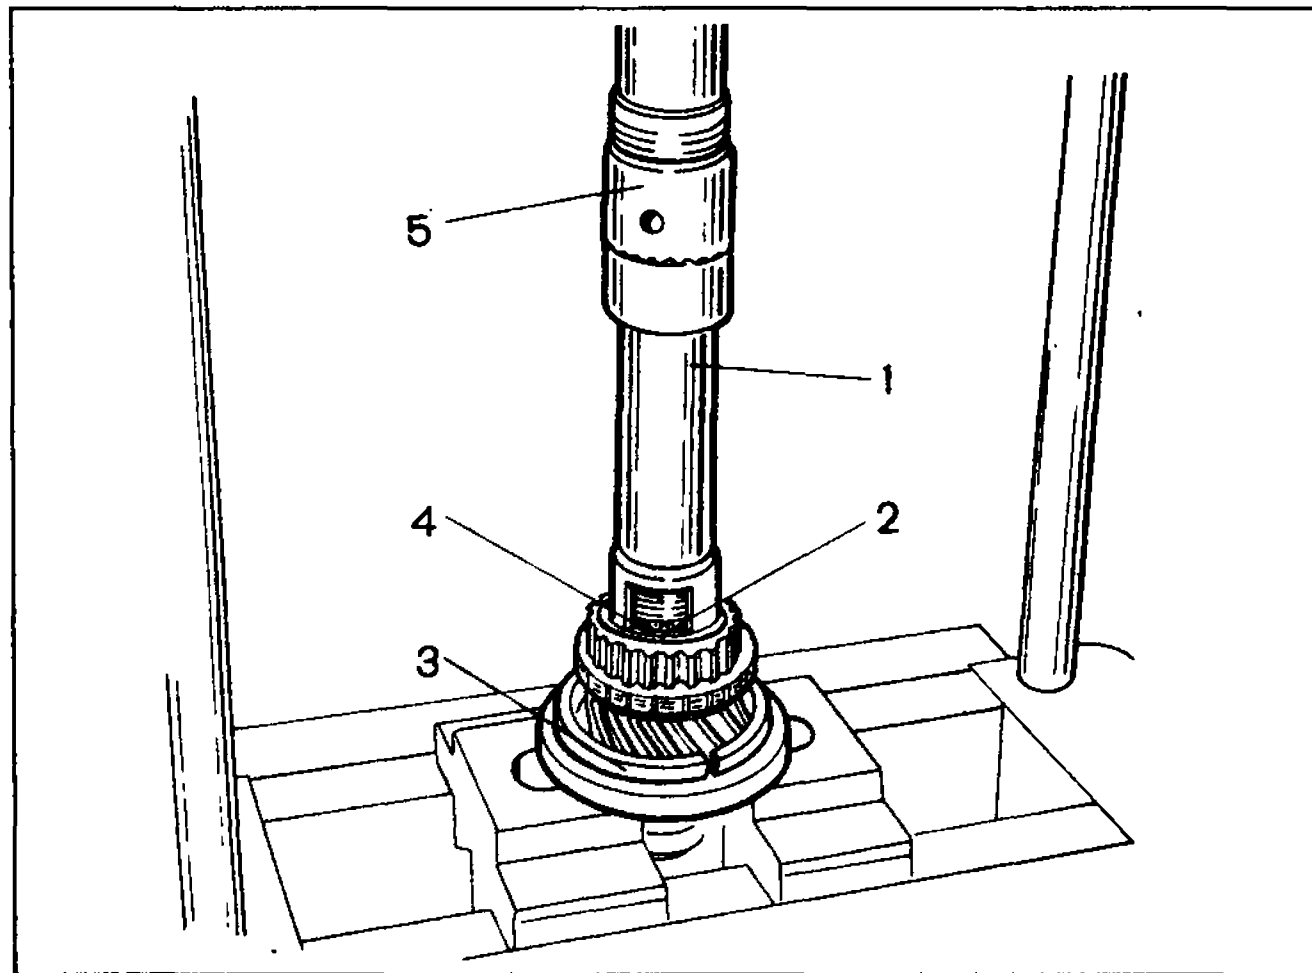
Снятие и установка на вторичном валу стопорного кольца: 1-оправка 41.7816.4069; 2-стопорное кольцо; 3-опорное полукольцо; 4-пружинная шайба; 5-шток пресса
